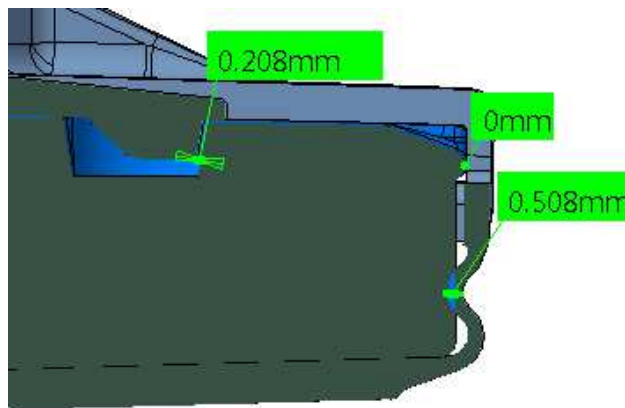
Konstrukční návrh – varianta 3: znázornění os a vertikální řez středem dílu.
